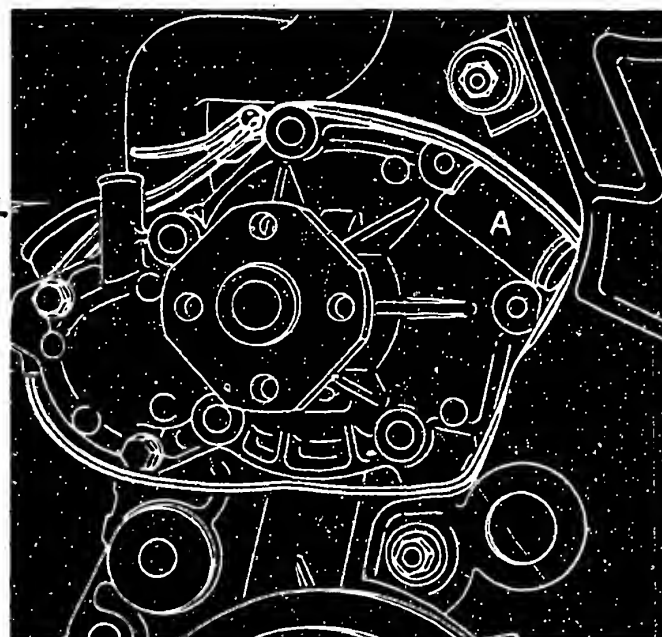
Dieselmotor J8S: Das Spannteil der Zahnriemen-Spannrolle (A) ist beim Ausbau der Wasserpumpe mit einer langen Bride zu sichern
